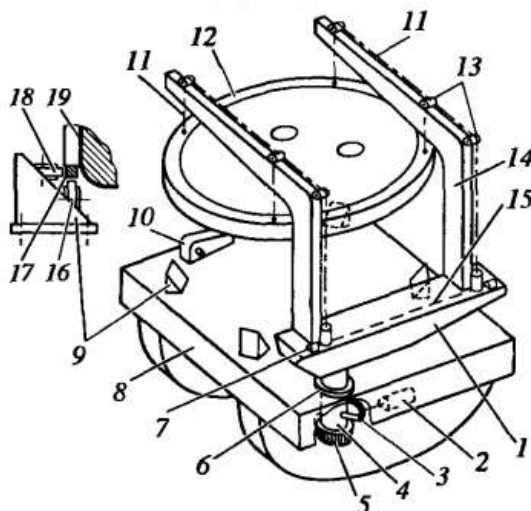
Механическое оборудование печи с опорой механизмов подъема — поворота свода на люльку
